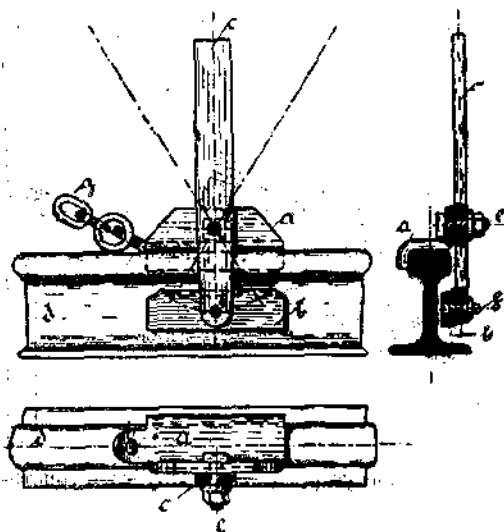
Тормозное устройство для спуска вагонеток с лесом.
